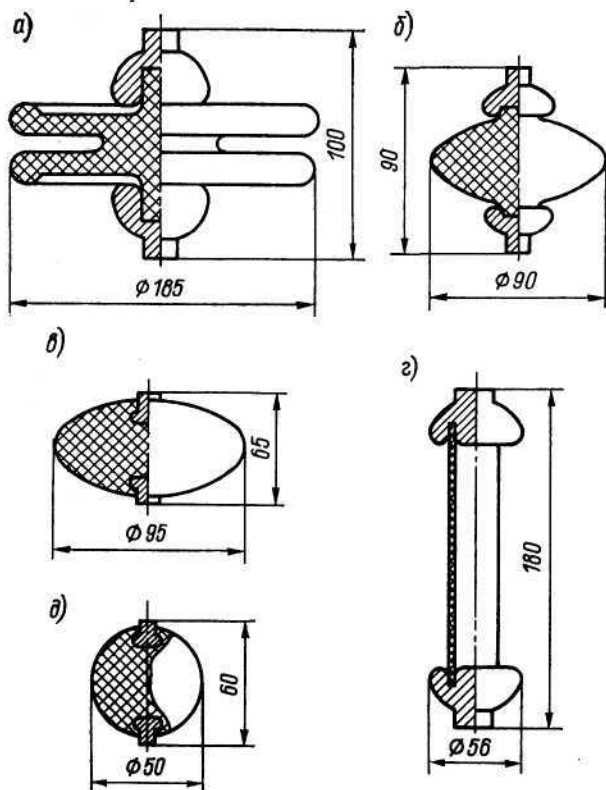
Поворотные изоляторы старой (а) и новой (б—д) конструкций
